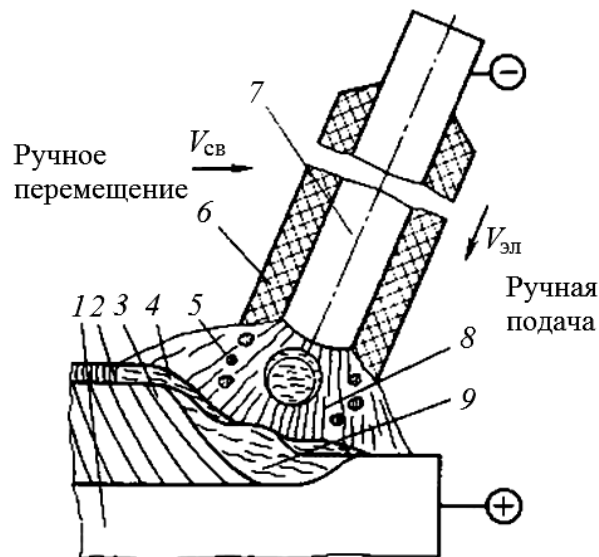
Схема процесса сварки металлическим покрытым электродом
